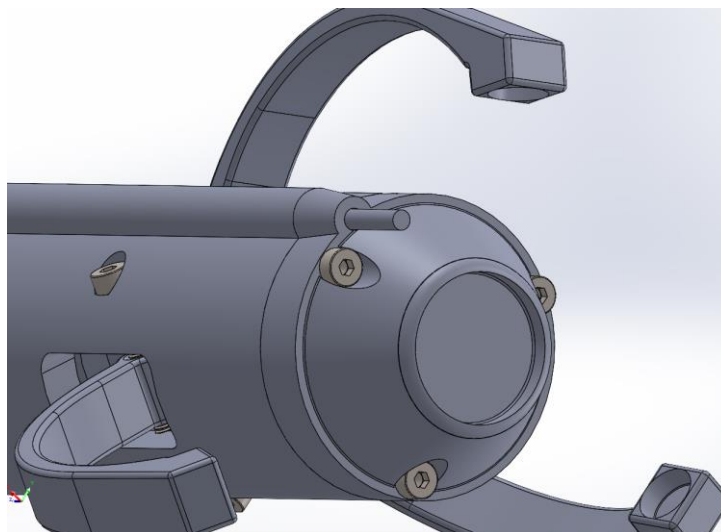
Posición de la tornillería en la pieza Unión para Correa.
